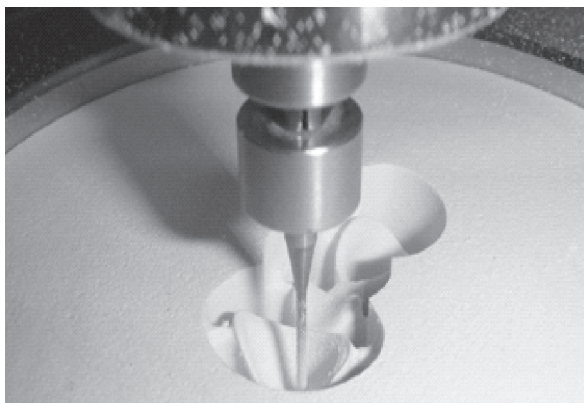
Етапи виготовлення ортопедичних конструкцій за допомогою фрезерувального апарата.
